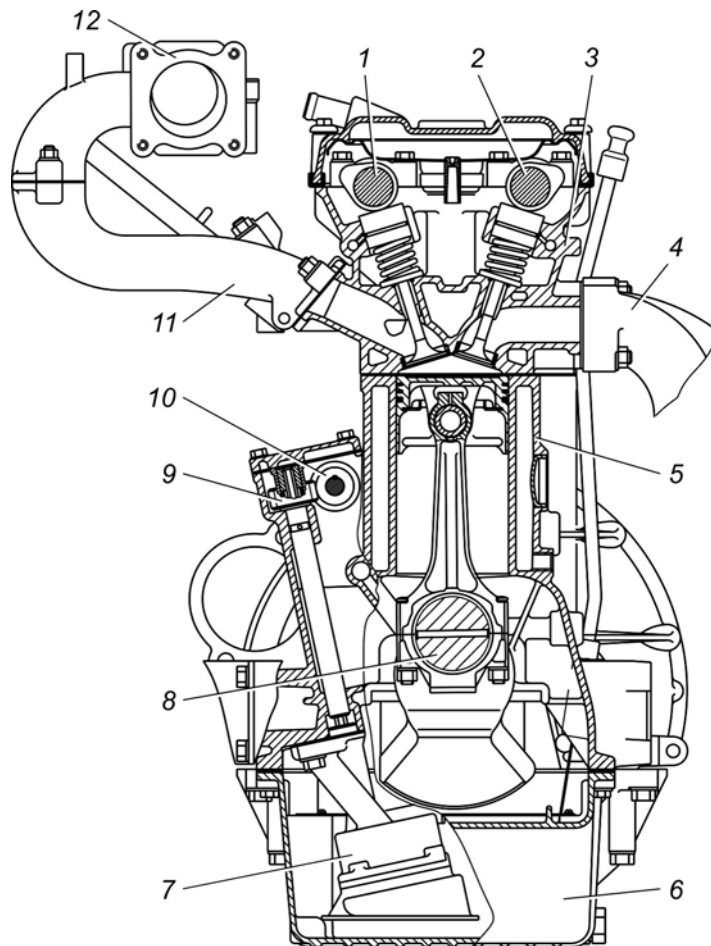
Поперечный разрез двигателя: 1 - распределительный вал впускных клапанов; 2 - распределительный вал выпускных клапанов; 3 - головка цилиндров; 4 - выпускной коллектор; 5 - блок цилиндров; 6 - масляный картер; 7 - масляный насос; 8 - коленчатый вал; 9 - шестерня привода масляного насоса ведомая; 10 - шестерня привода масляного насоса ведущая; 11 - впускная труба; 12 - ресивер
